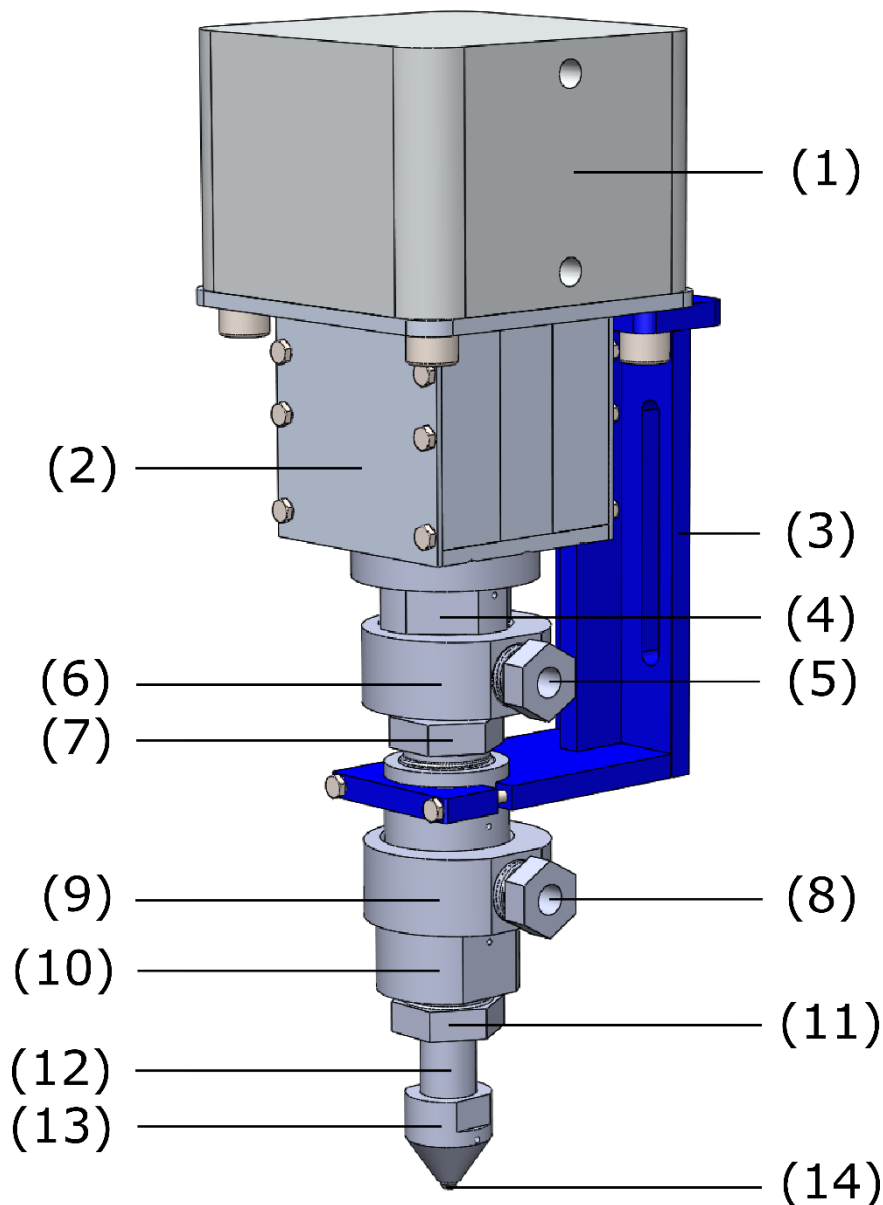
CAD-Ansicht der Ventilbaugruppe; (1) Pneumatikkompaktzylinder; (2) Federpaketgehäuse; (3) Ventilhalterung; (4) oberes Ventilgehäuse; (5) Druckschraube Spülstrom; (6) Anschlussring Spülstrom; (7) 11/16"-Hochdruckverschraubung; (8) Druckschraube Schneidsuspension; (9) Anschlussring Schneidsuspension; (10) unteres Ventilgehäuse; (11) 11/16"-Hochdruckverschraubung; (12) Kollimationsrohr; (13) Düsenhalter; (14) Hartmetalldüse
